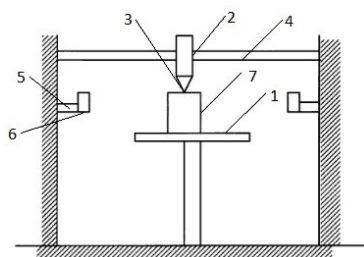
Печать модели: 1 – рабочий стол, 2 – печатающая головка, 3 – сопло, 4 – направляющая по оси Y, 5 – держатель очистителя сопла, 6 – очиститель сопла, 7 – печатающая деталь
